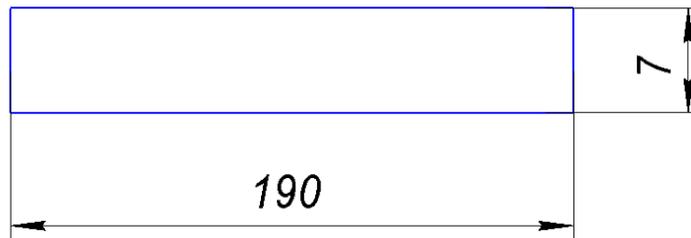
Эскиз поверхности, обработанной чистовым фрезерованием.
